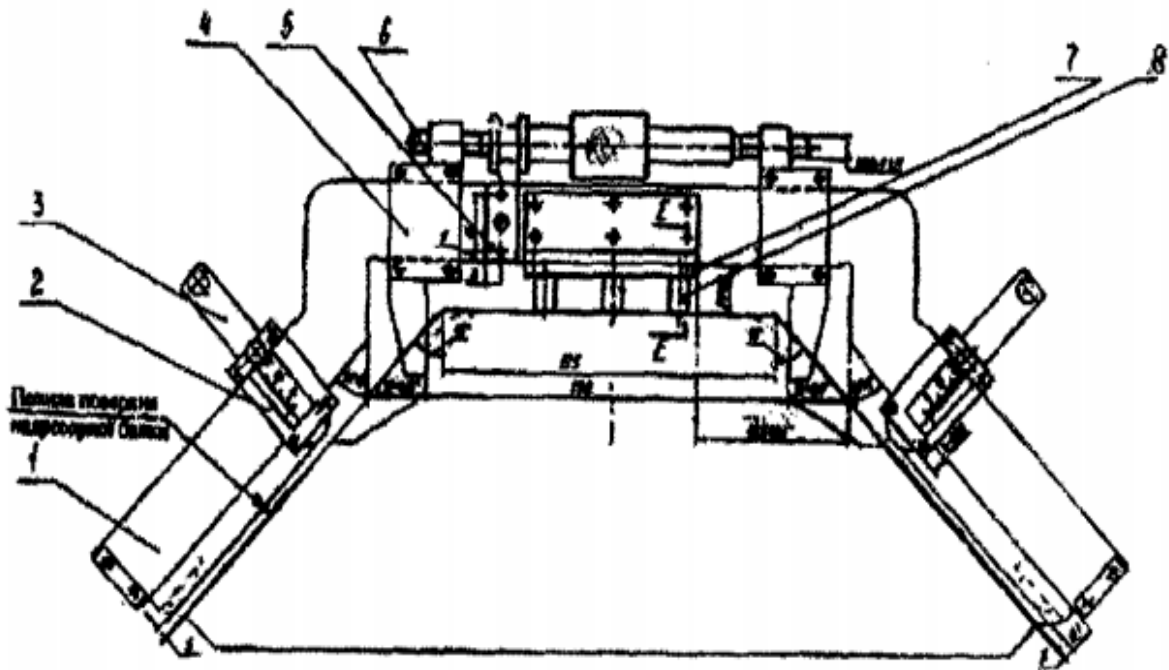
Вимірювач похилих поверхонь надресорної балки
